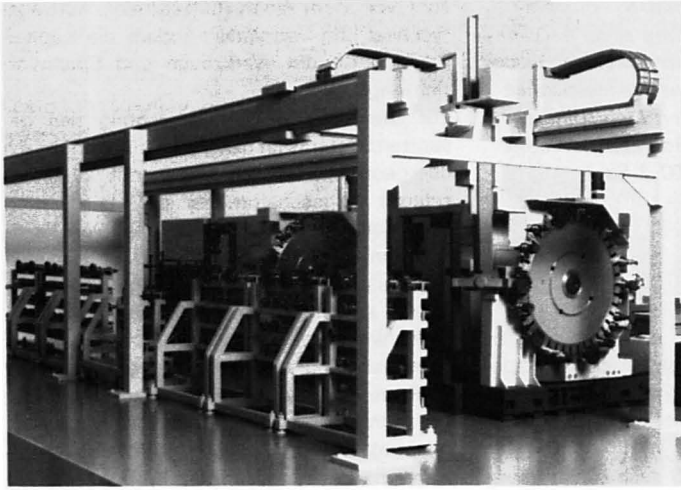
Integrierte automatische Werkzeugversorgung mit erweiterungsfähigem Werkzeugmagazin in einem flexiblen Fertigungssystem (Bauart Werner)
